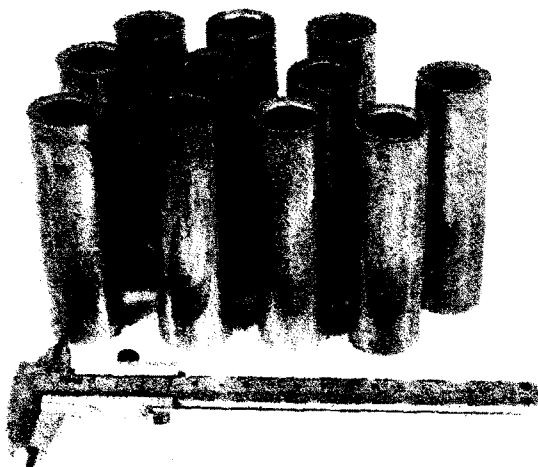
Стаканы, изготовленные выдавливанием из спеченных порошковых заготовок
